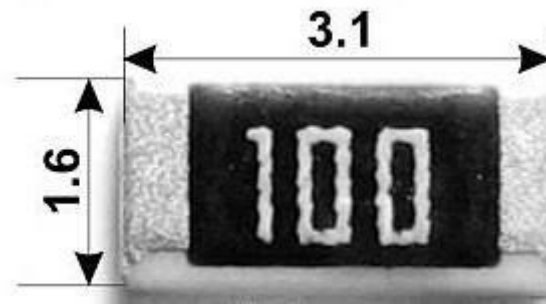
зовнішній вигляд і розміри корпусу SMD1206
